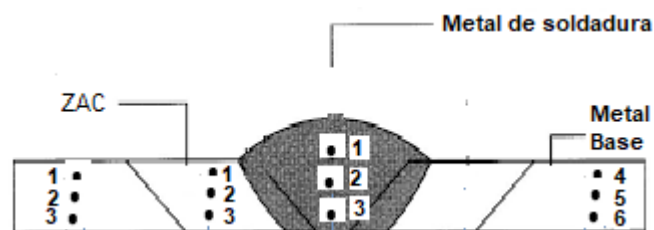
Puntos a medir del material base, la zona ZAC y la zona de soldadura.
